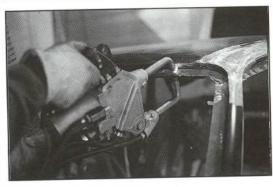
Equipos de soldadura MIG/MAG y por puntos de resistencia.
